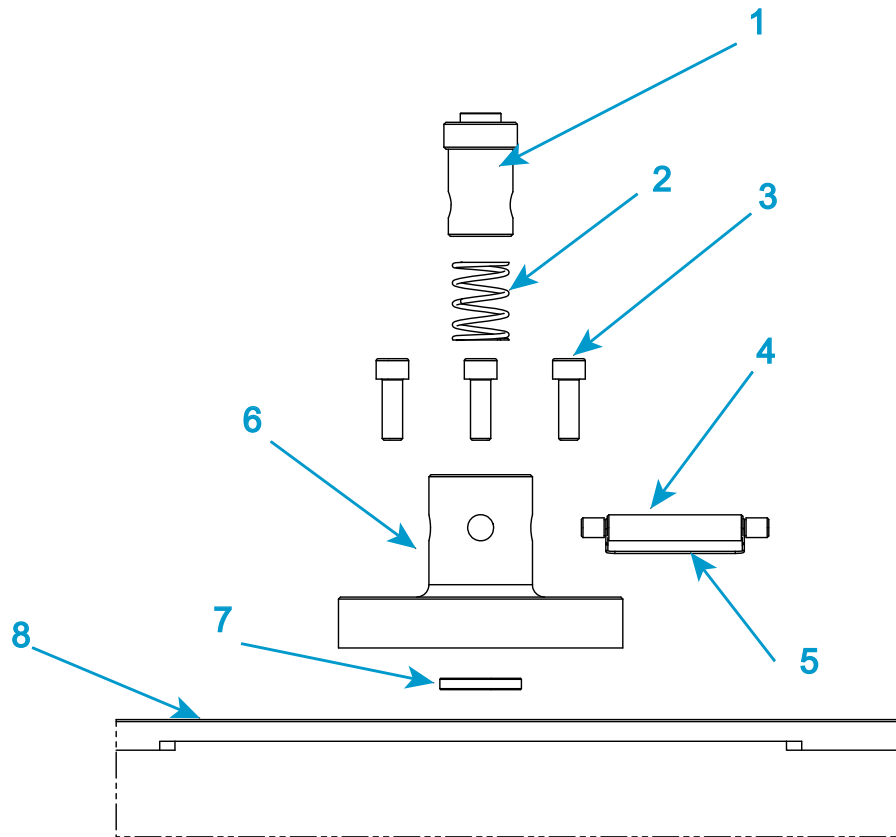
Sockeladapter Typ D - 68TM-30, 68TM-50 und 68TM-100
